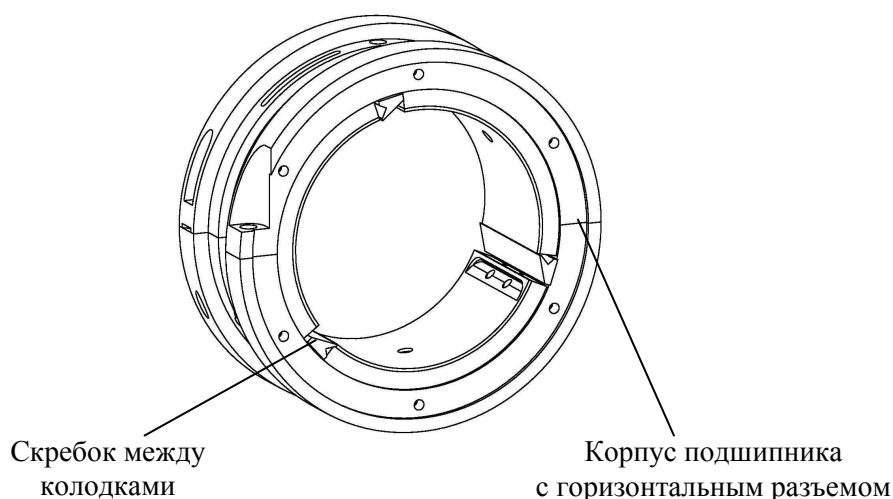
Модернизированный демпферный опорный подшипник на гидростатической пленке
